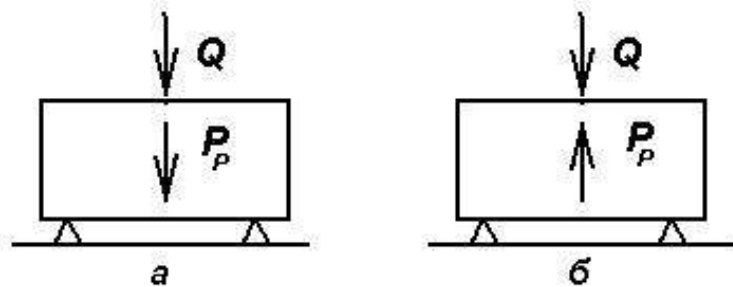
Розрахункові схеми при притиску заготовки до опор та відриву від опор
